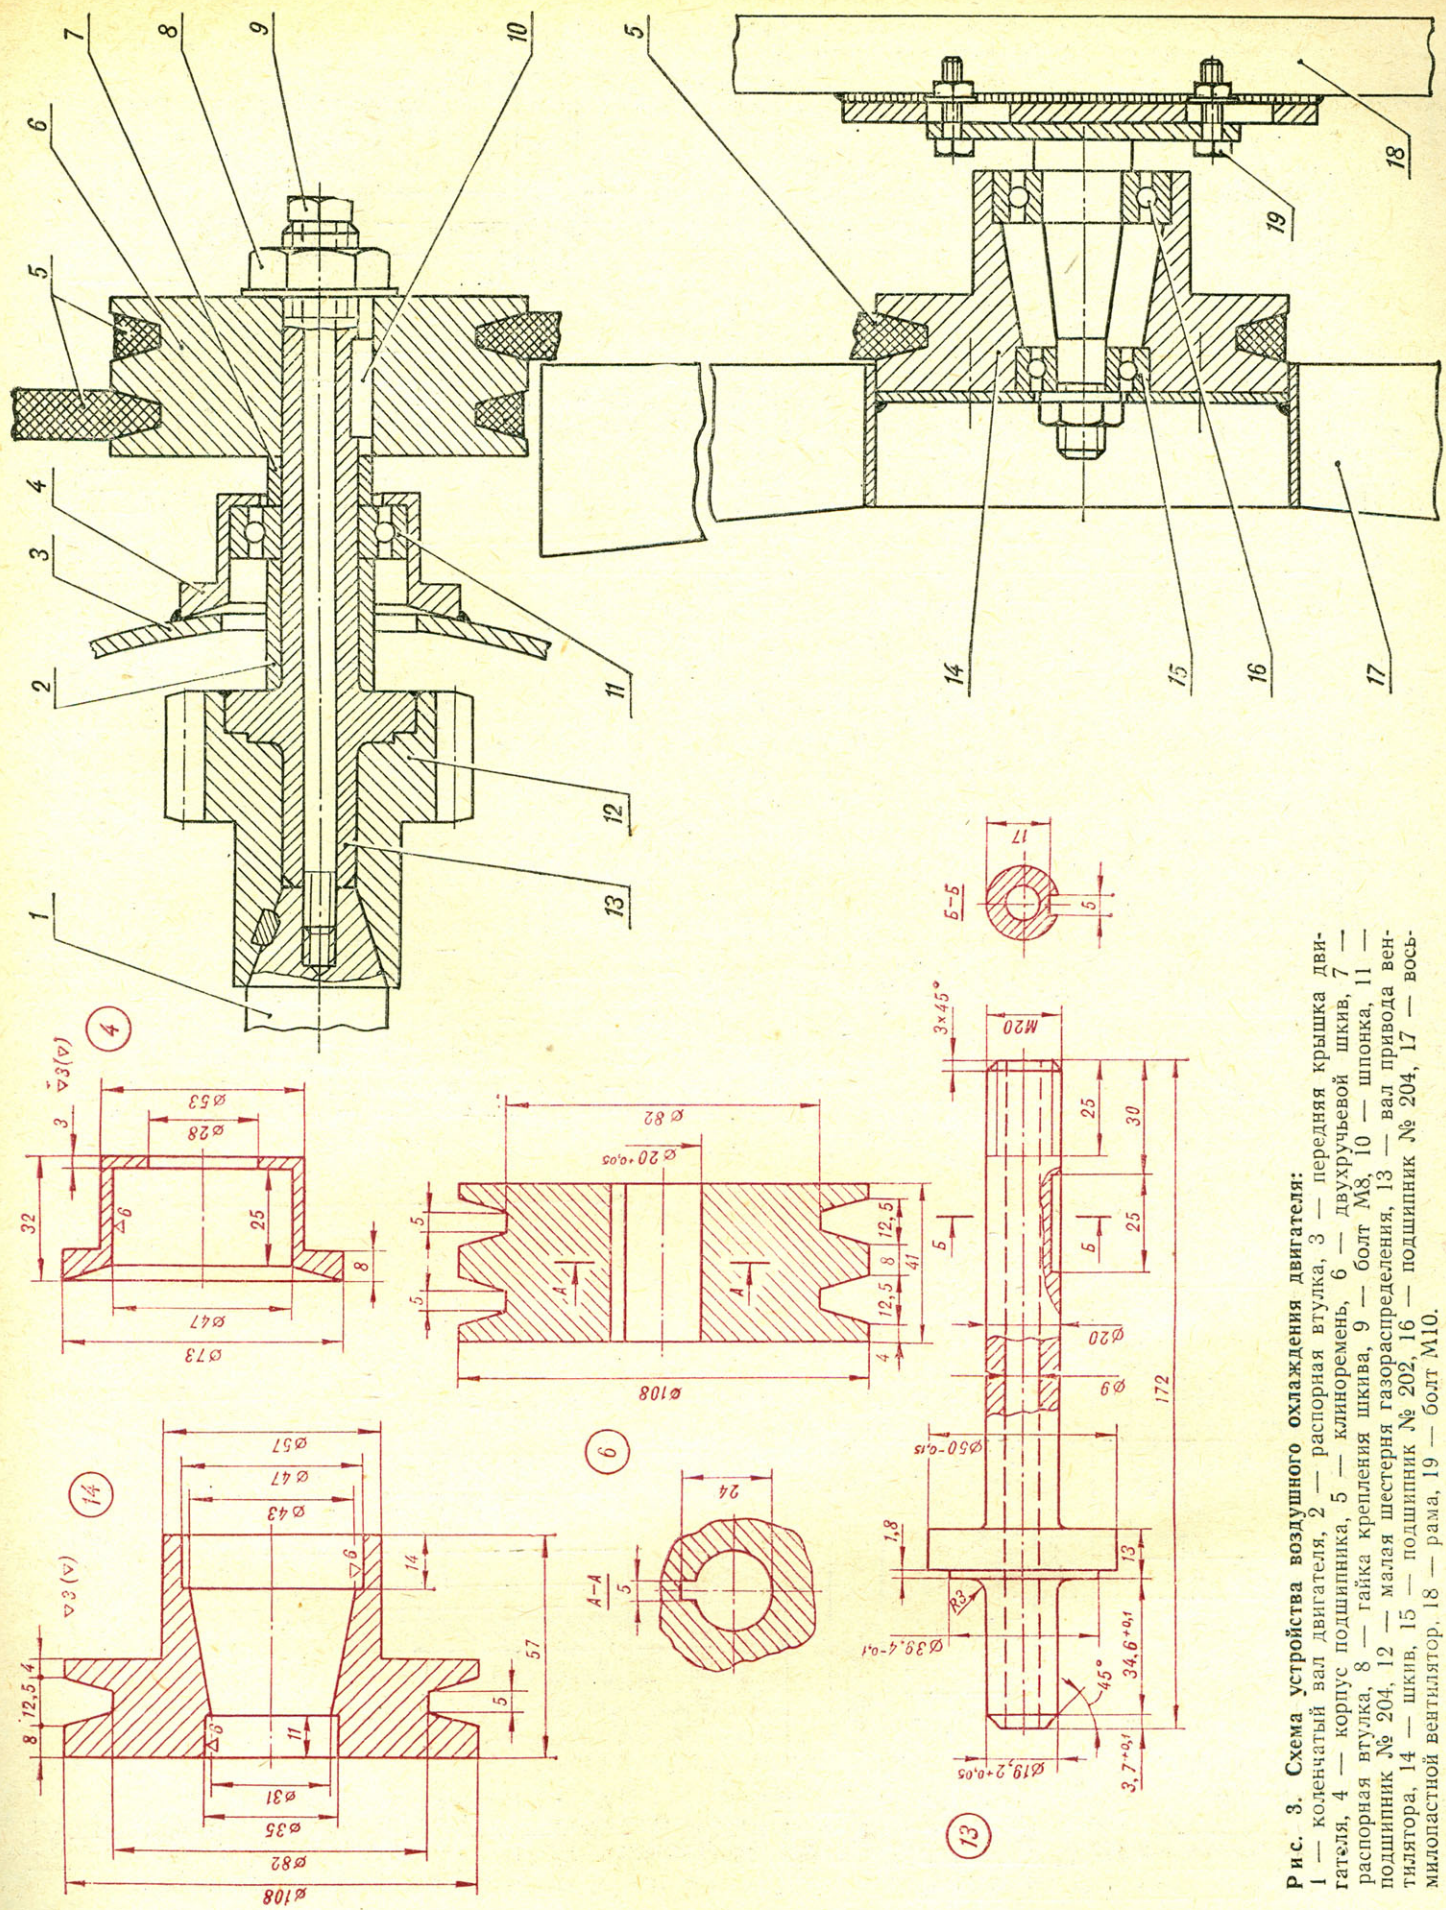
Схема устройства воздушного охлаждения двигателя: 1 — коленчатый вал двигателя, 2 — распорная втулка, 3 — передняя крышка двигателя, 4 — корпус подшипника, 5 — клиноремень, 6 — болт М8, 7 — распорная втулка, 8 — гайка крепления шкива, 9 — шпонка, 10 — шпонка, 11 — подшипник № 204, 12 — малая шестерня газораспределения, 13 — вал привода вентилятора, 14 — шкив, 15 — подшипник № 202, 16 — подшипник № 204, 17 — восьмилопастной вентилятор, 18 — рама, 19 — болт М10.
